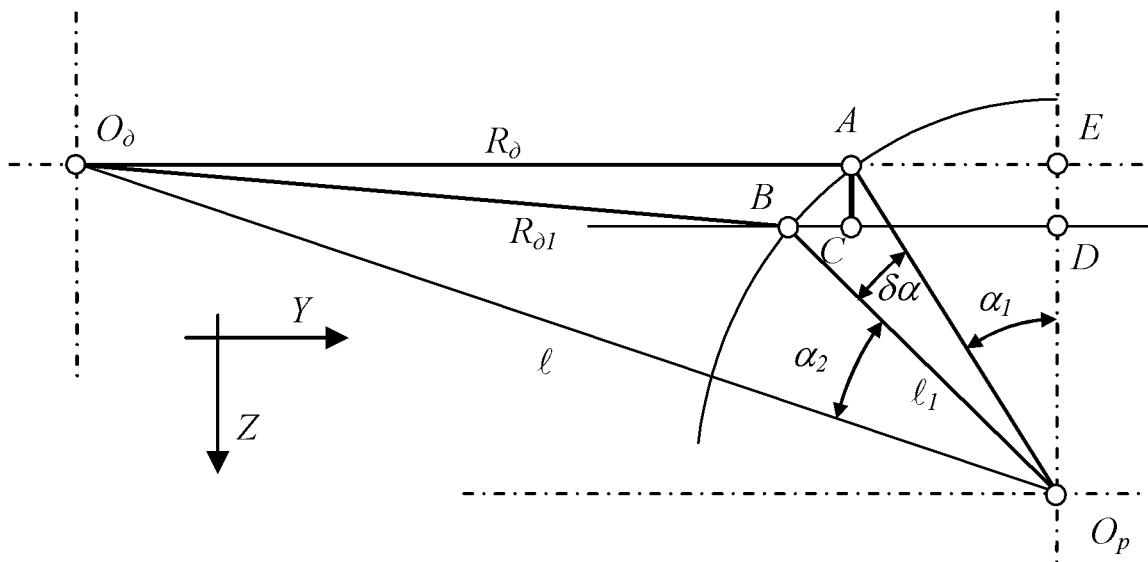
Розрахункова схема компенсації похибки обробки
